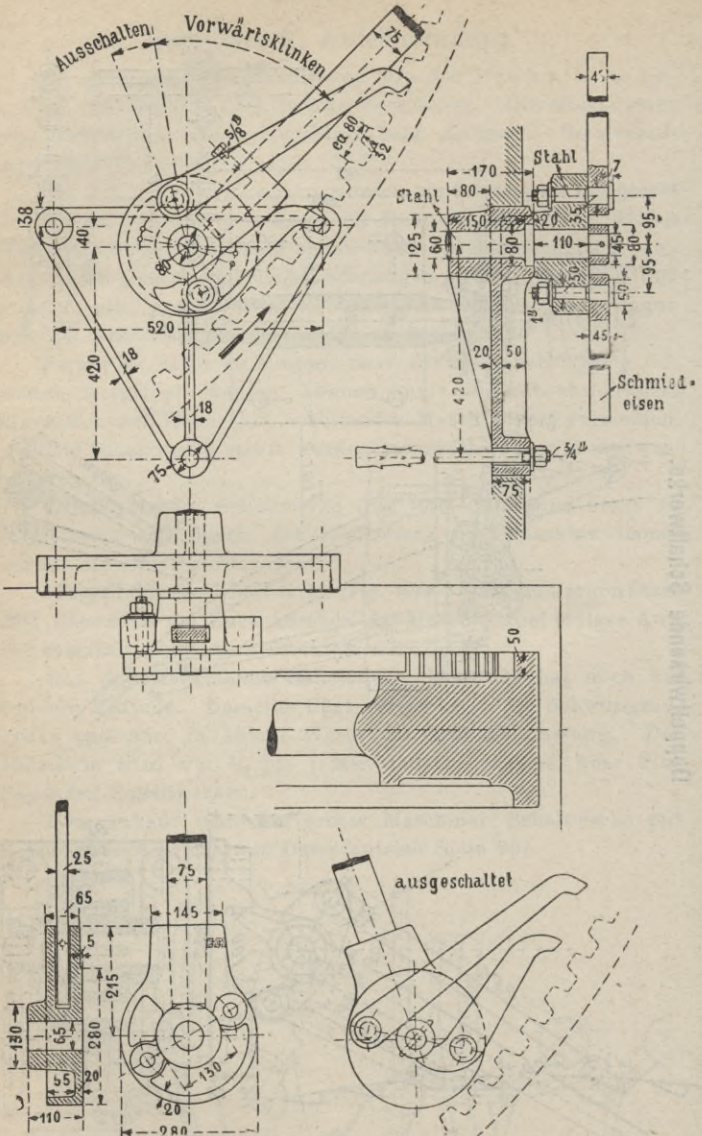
1026 für 900 bis 1100 mm Kolbenhub.
